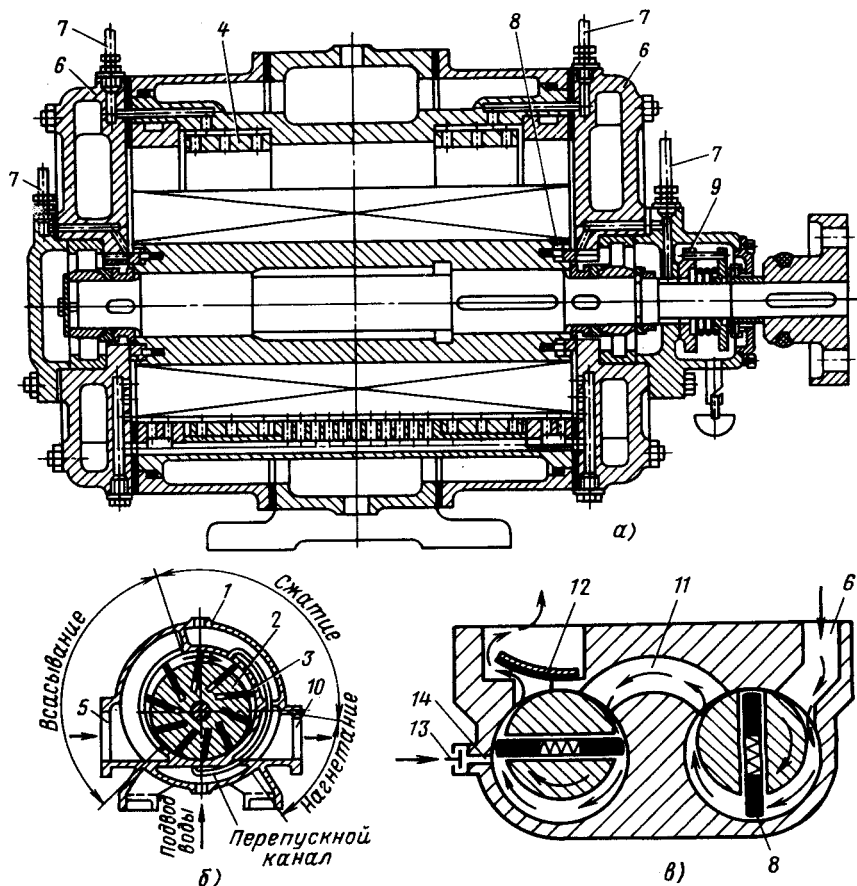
Разрезы (а, б) многопластинчатого ВН и схема (в) двух-
